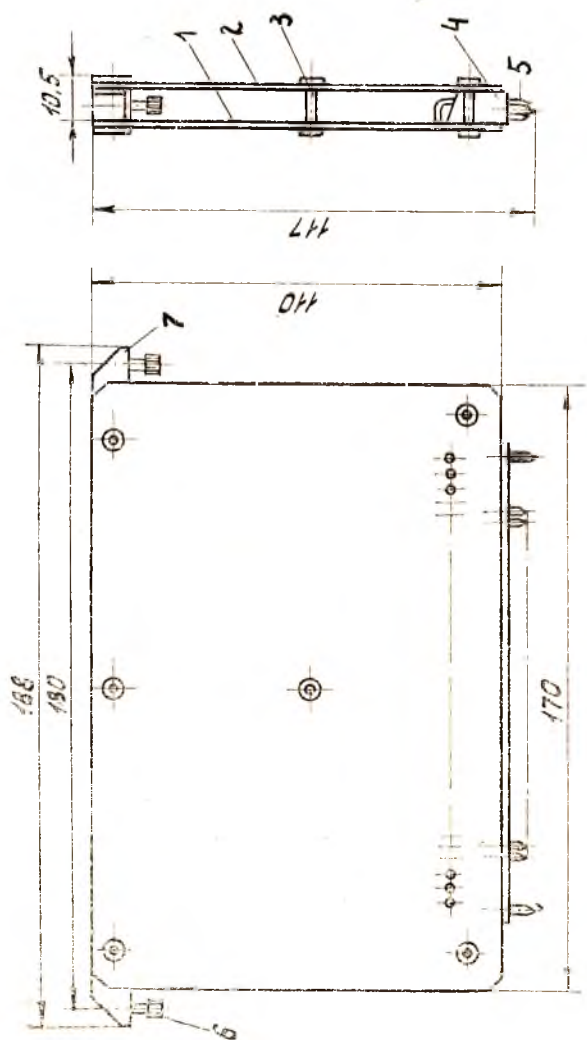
Двухслойная кассета блока разъемной конструкции в безрамочном исполнении: 1 и 2 — печатные платы; 3 — колонка; 4 — вилка соединителя; 5 — штырь-ловитель; 6 — невыводящийся винт; 7 — накладка
